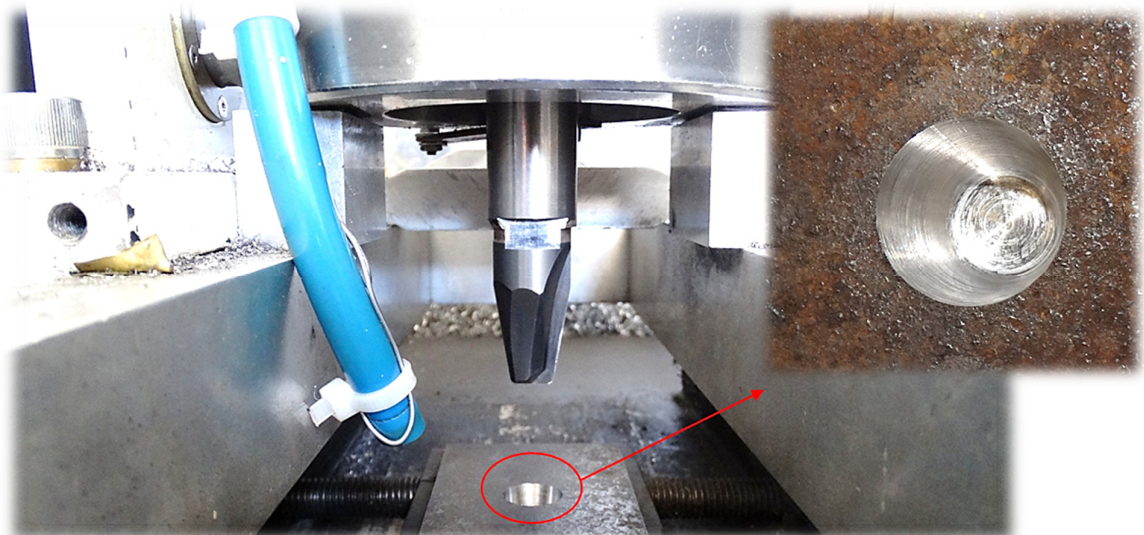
Usinagem do furo realizado com a fresa cônica.
